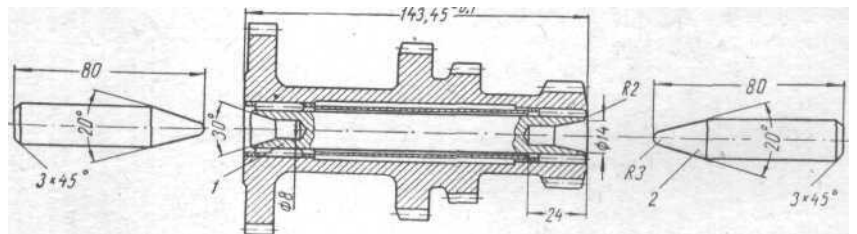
Оправки для выпрессовывания и запрессовывания оси блока шестерен промежуточного вала
